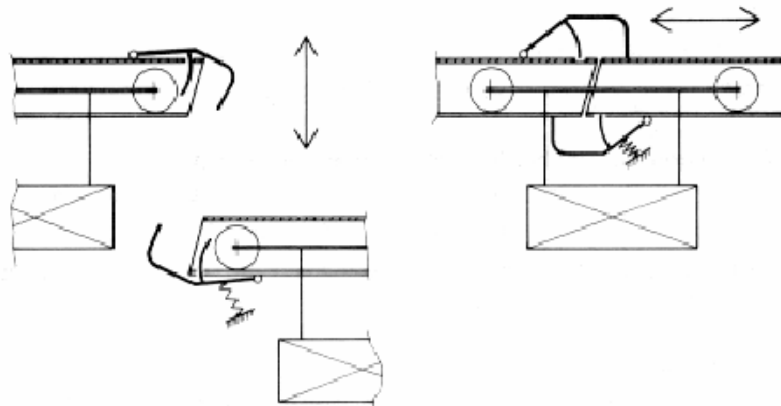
Prinzip einer mechanisch gesteuerten Sperre in einem Schienenstück.
